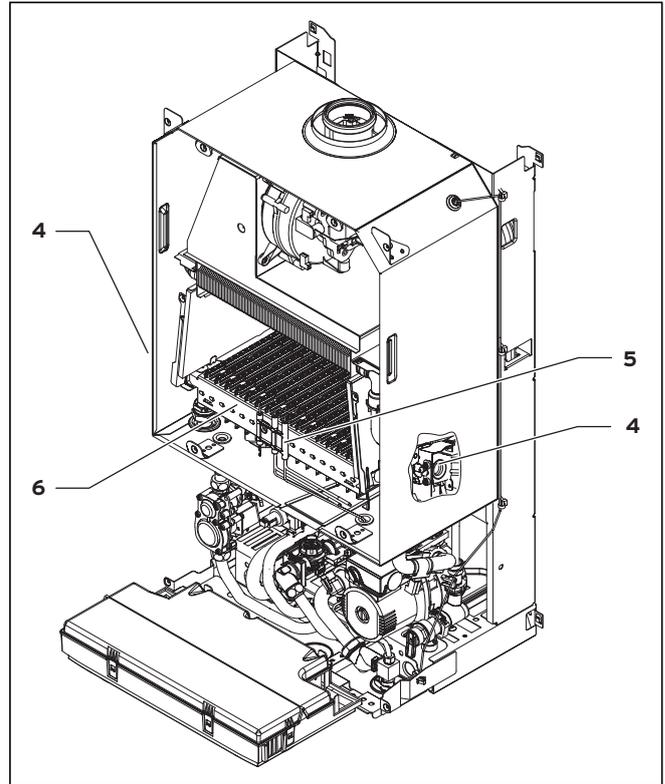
Limpieza del quemador con desmontaje (suciedad severa)
